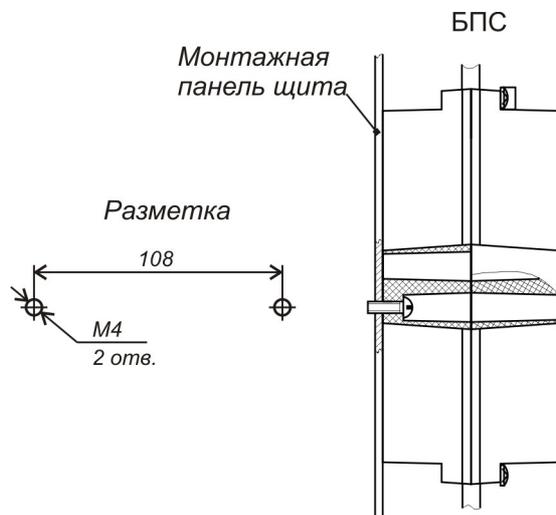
Установка БПС на монтажной панели корпуса Rх
